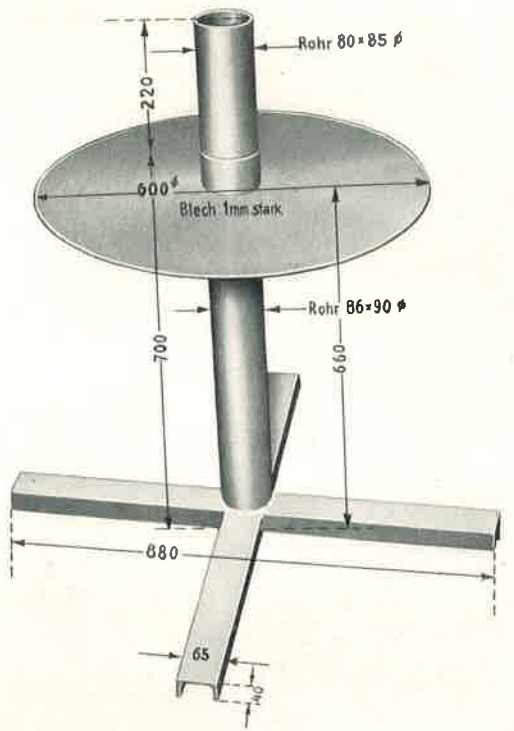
/1: Für gleichzeitiges Arbeiten am Motor und Getriebe sollten möglichst zwei Montagetische vorhanden sein. Montagetisch schräg von oben gesehen.
